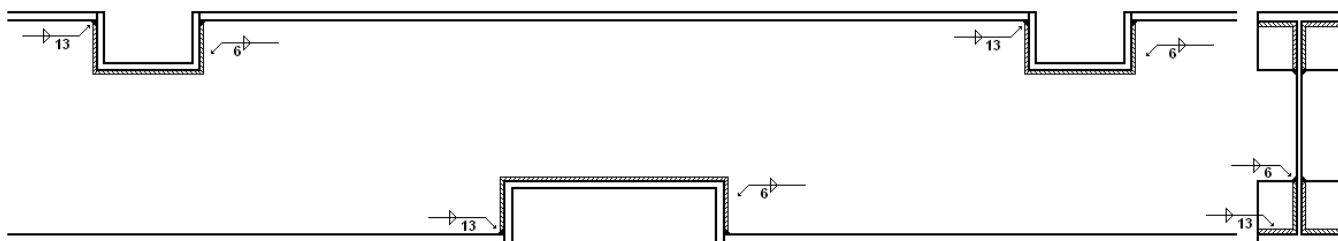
Soldadura das chapas de apoio das unidades de pesagem e passagem do pórtico
